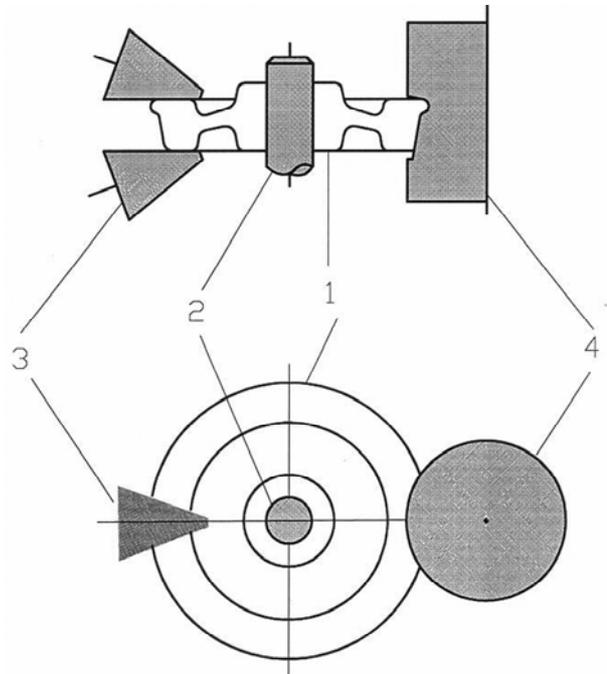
Схема прокатки колеса на кольцебандажном стане:
